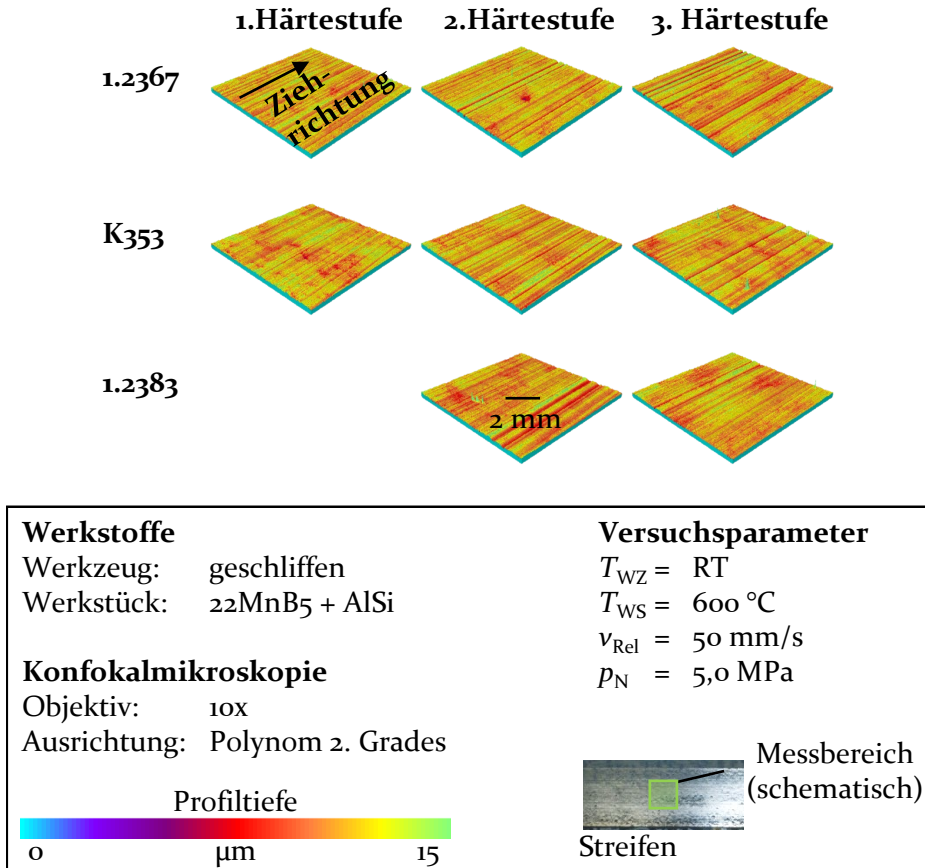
Topographieaufnahmen der Werkstückoberfläche für unterschiedliche Werkzeug-härte
